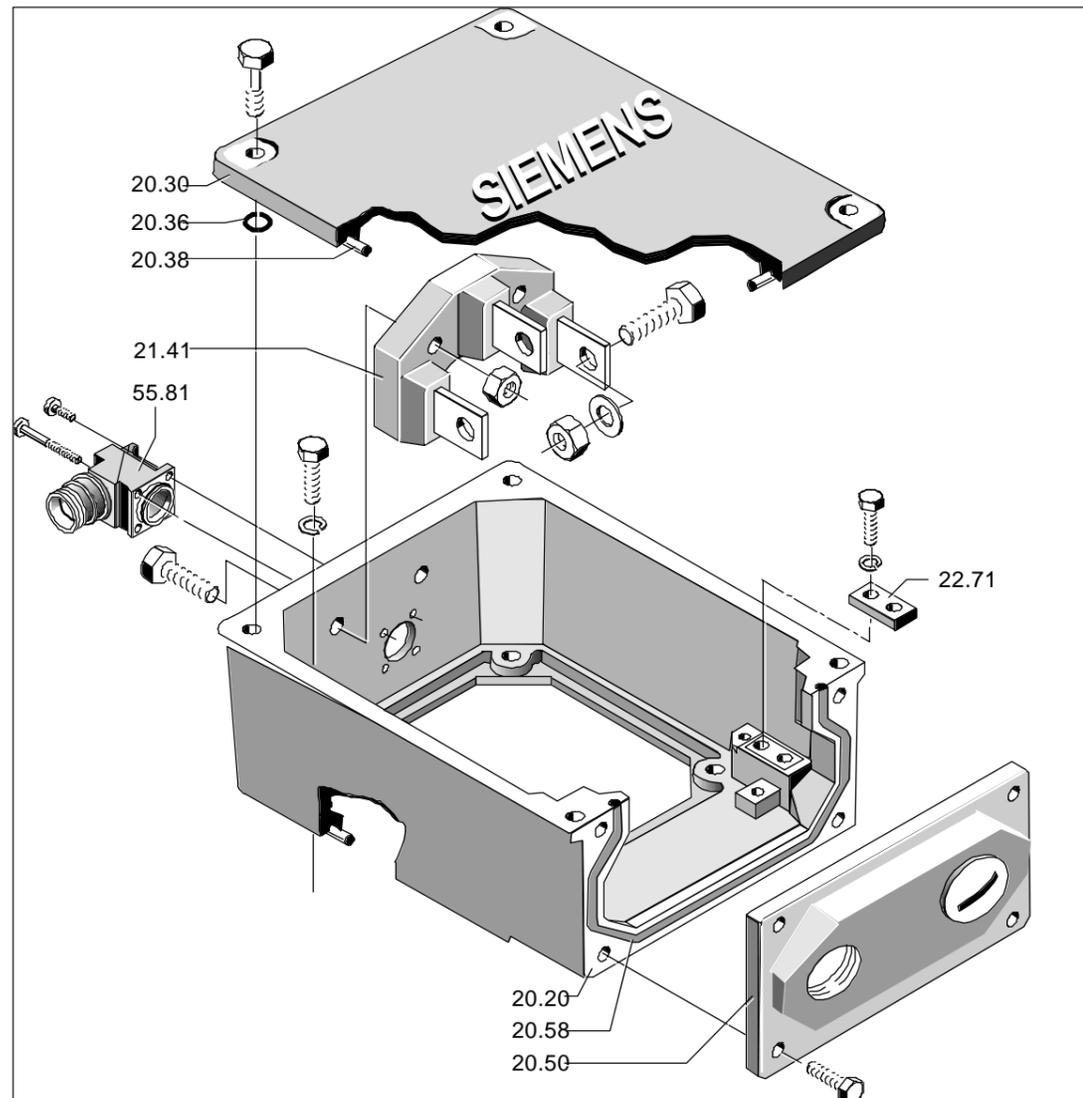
c: Klemmenkasten (Beispiel, gelieferte Ausführung kann im Detail abweichen)
